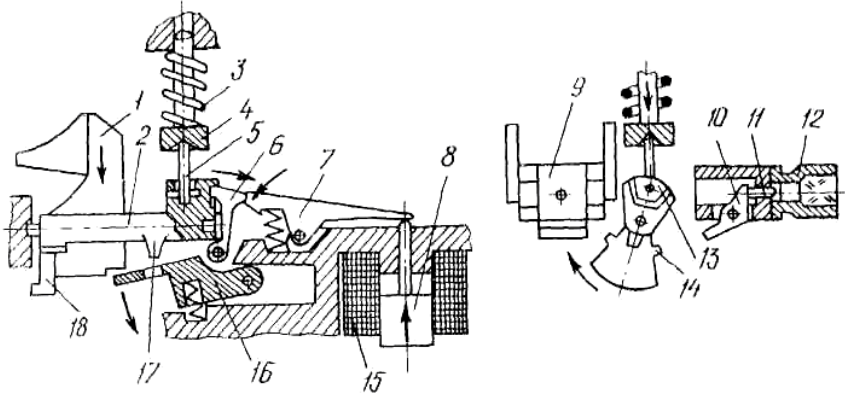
Стріляючий механізм гармати ГШ-23
